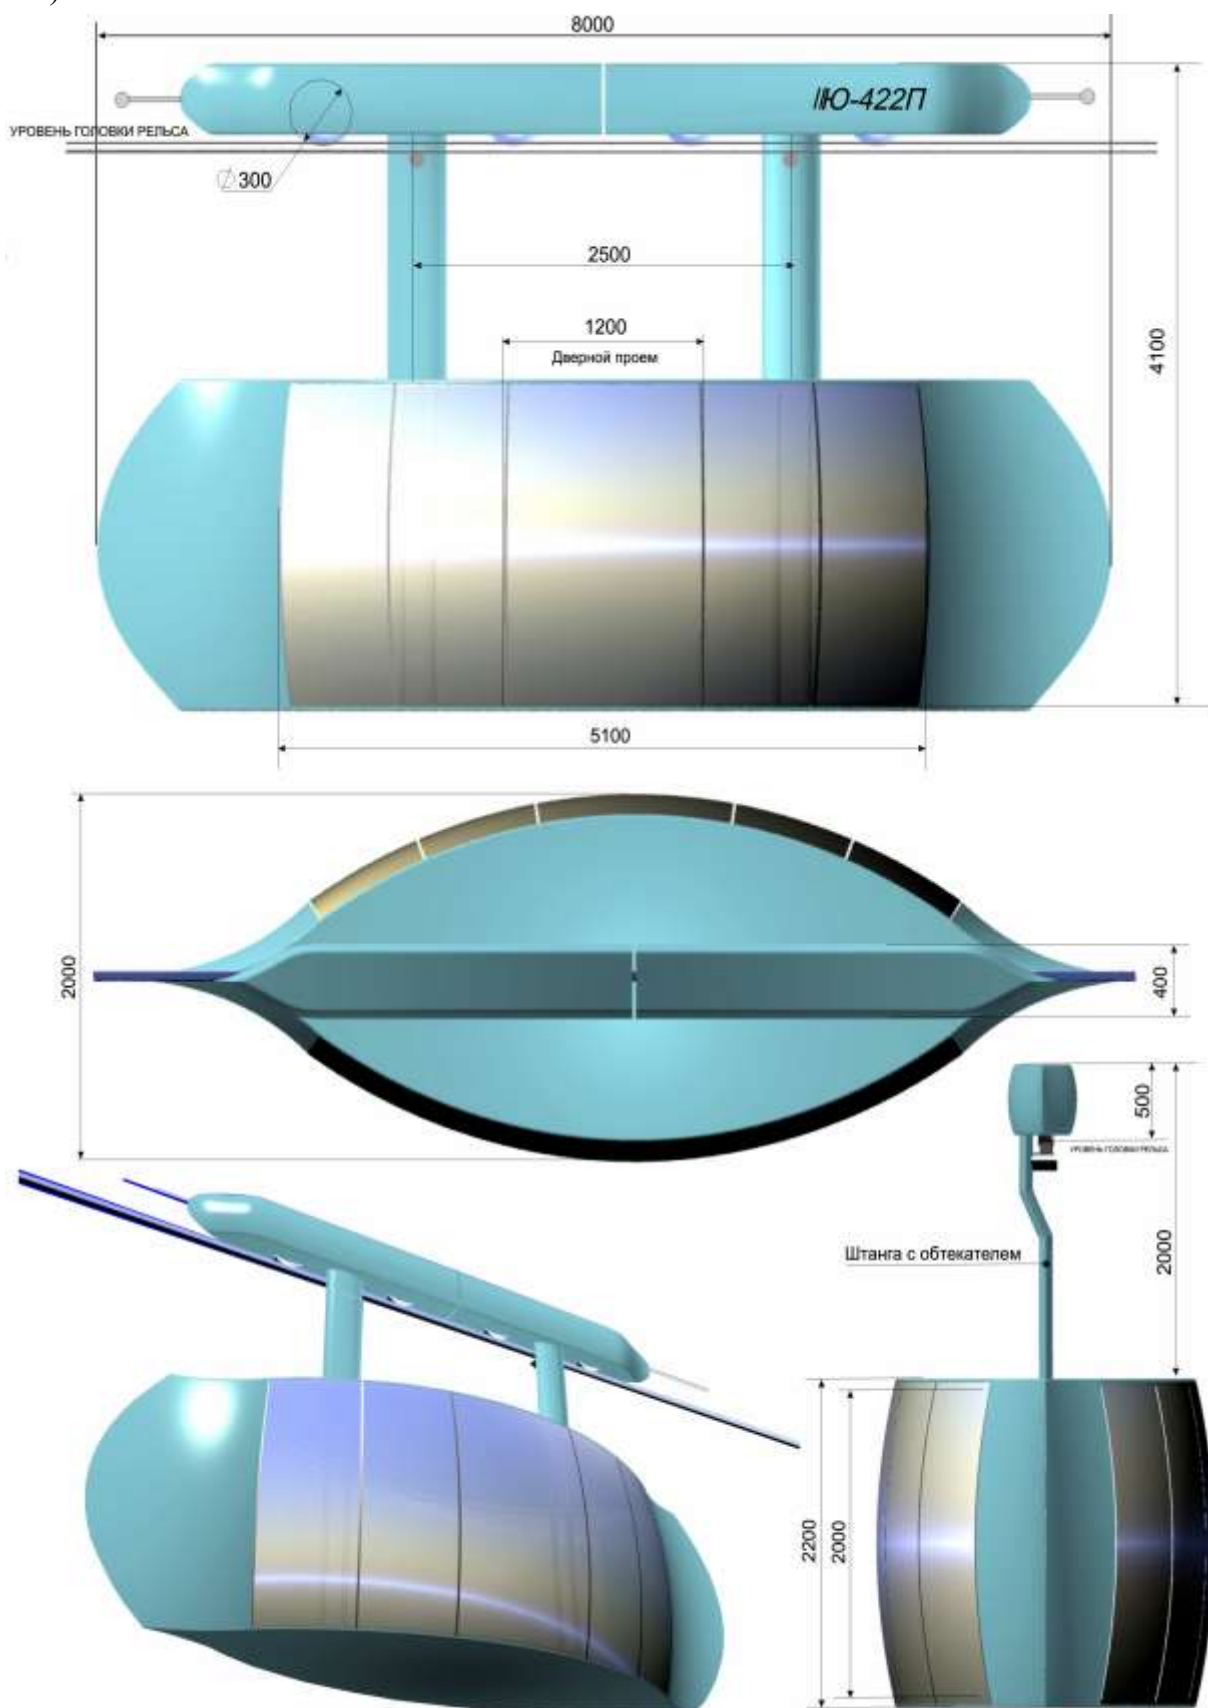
Внешний вид и габаритные размеры моно-юнибуса Ю-422П
